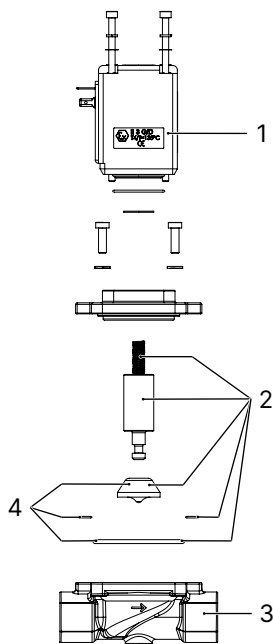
Vue d'ensemble des pièces de rechange pour l'électrovanne Type 0283
